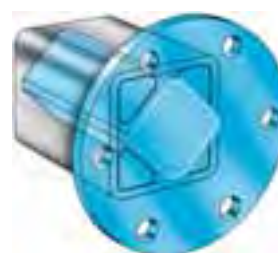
Perfil quadrado soldado a uma flange
